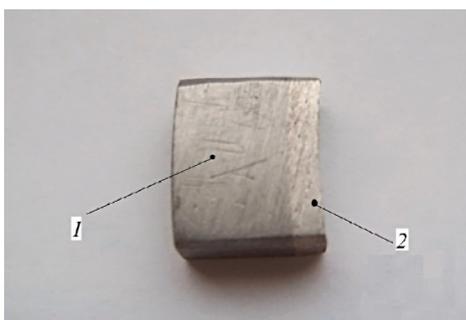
Образец № 1, стандартный: 1 – сталь; 2 – баббит Б-83
